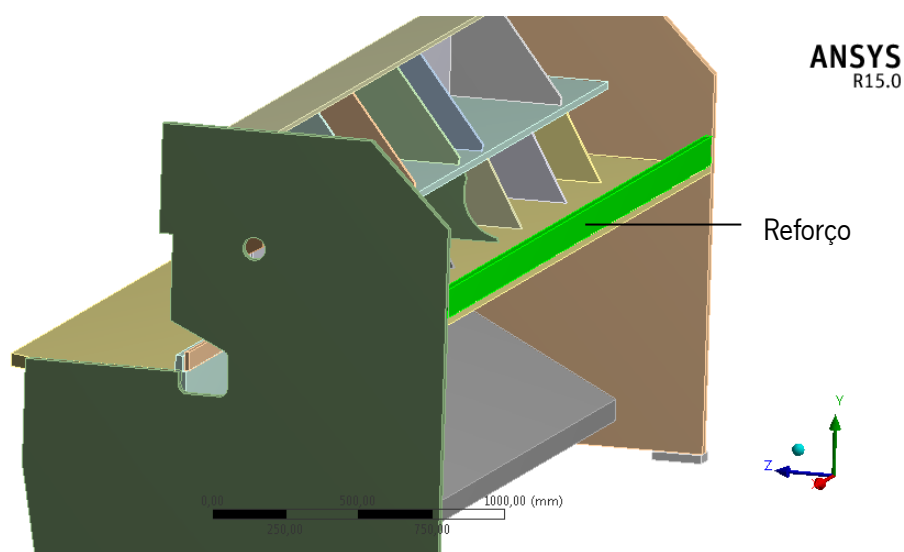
Detalhe do pormenor do perfil de secção retangular.
